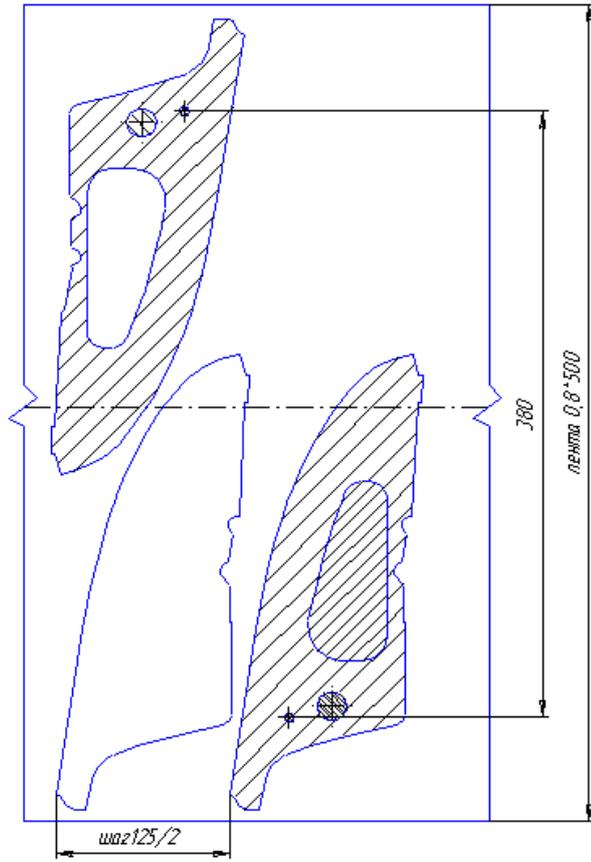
Оп. 10 Вырубка-пробивка
